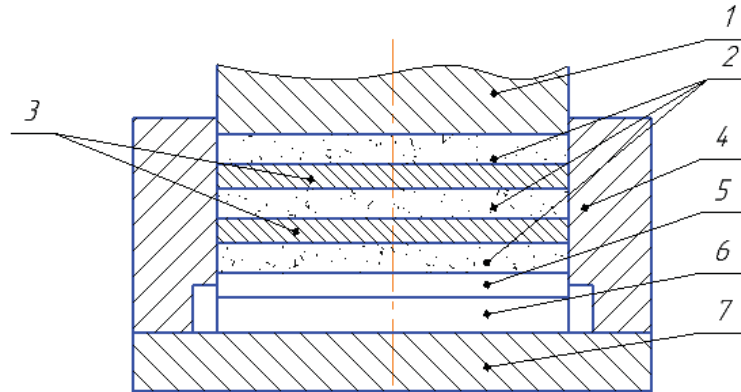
Схема пакетного прессования: 1 – пуансон; 2 – порошковая композиция; 3 – стальная прокладка; 4 – матрица; 5 – основание
